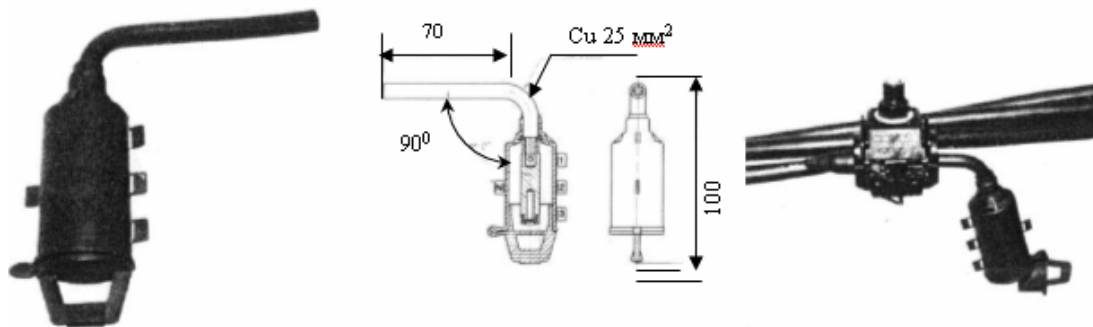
Изолированный адаптер для закороток и заземления СИП типа РМСС
